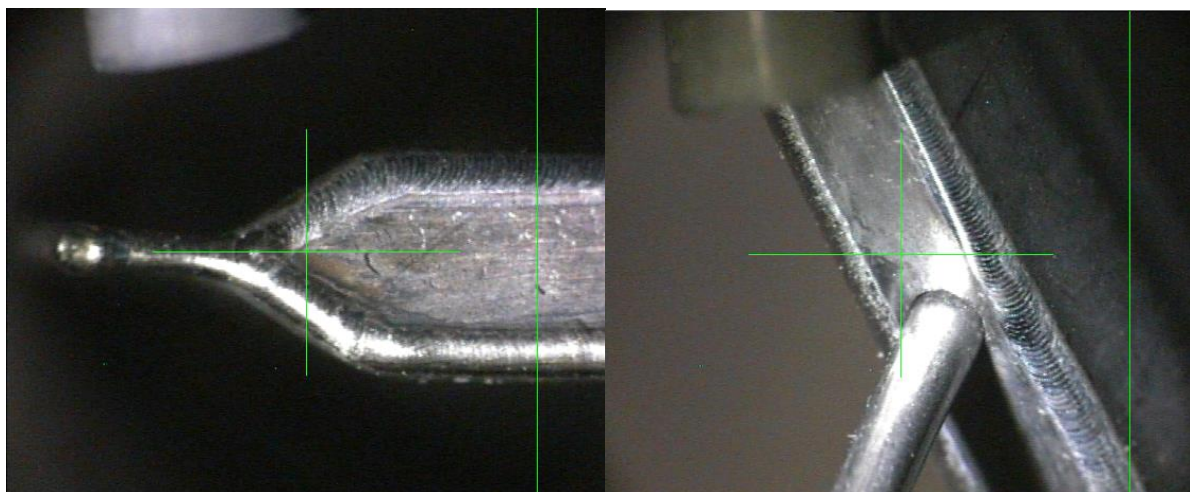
Внешний вид сварки конверта для испытаний
